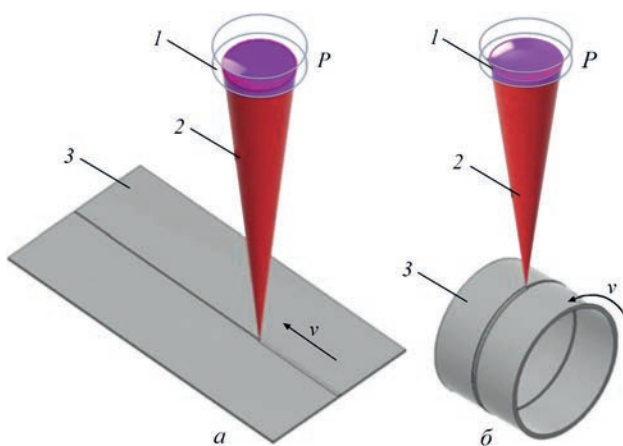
Схеми лазерного зварювання: стикових зварних з'єднань (а), кільцевих зварних з'єднань (б): 1 – лінза, 2 – лазерний промінь, 3 – зварювані деталі
